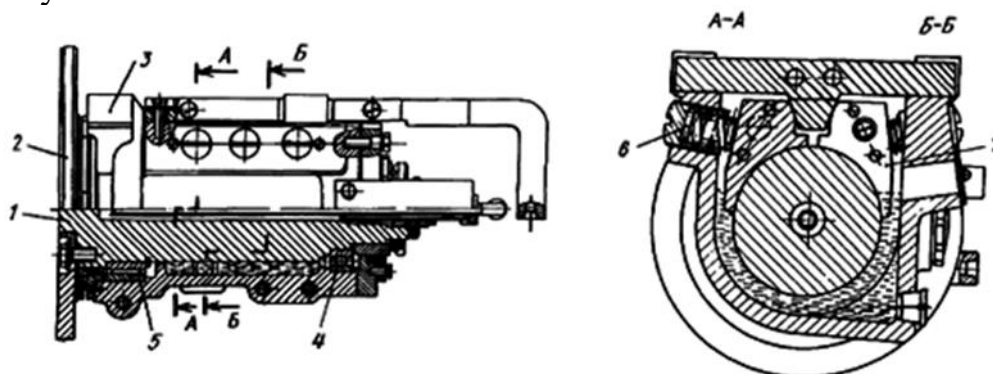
Скользящий токоподвод машины шовной сварки
